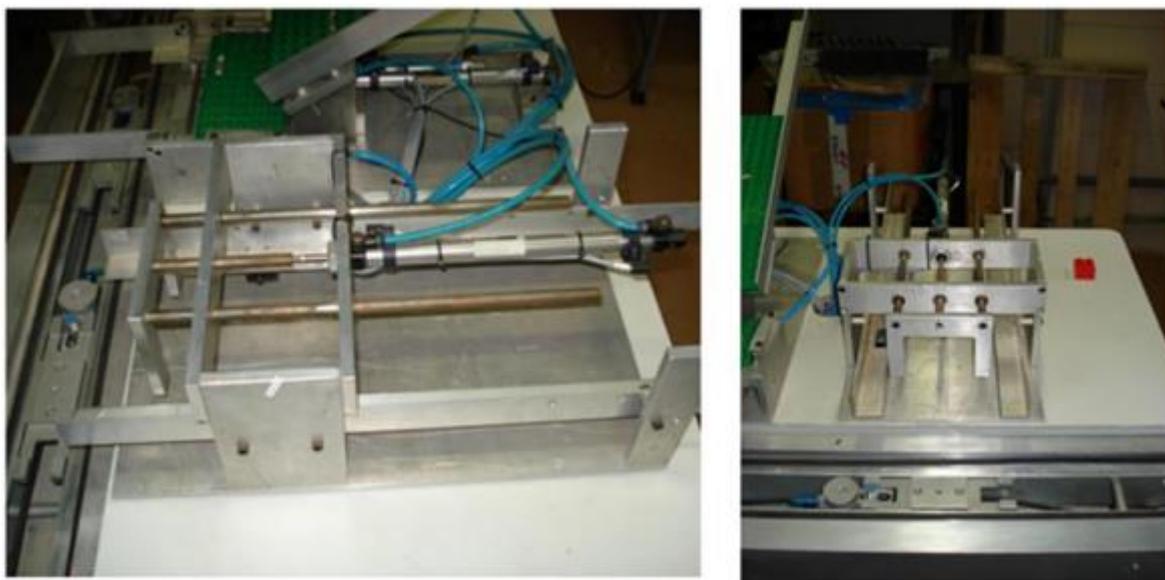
Módulo de Descarregamento da Peça. Fonte: SILVERIA JUNIOR (2016)
